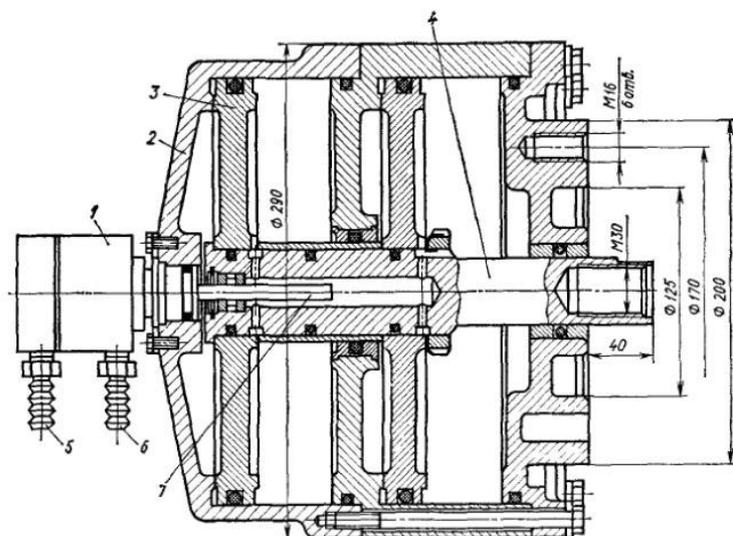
Вращающийся сдвоенный пневмоцилиндр
